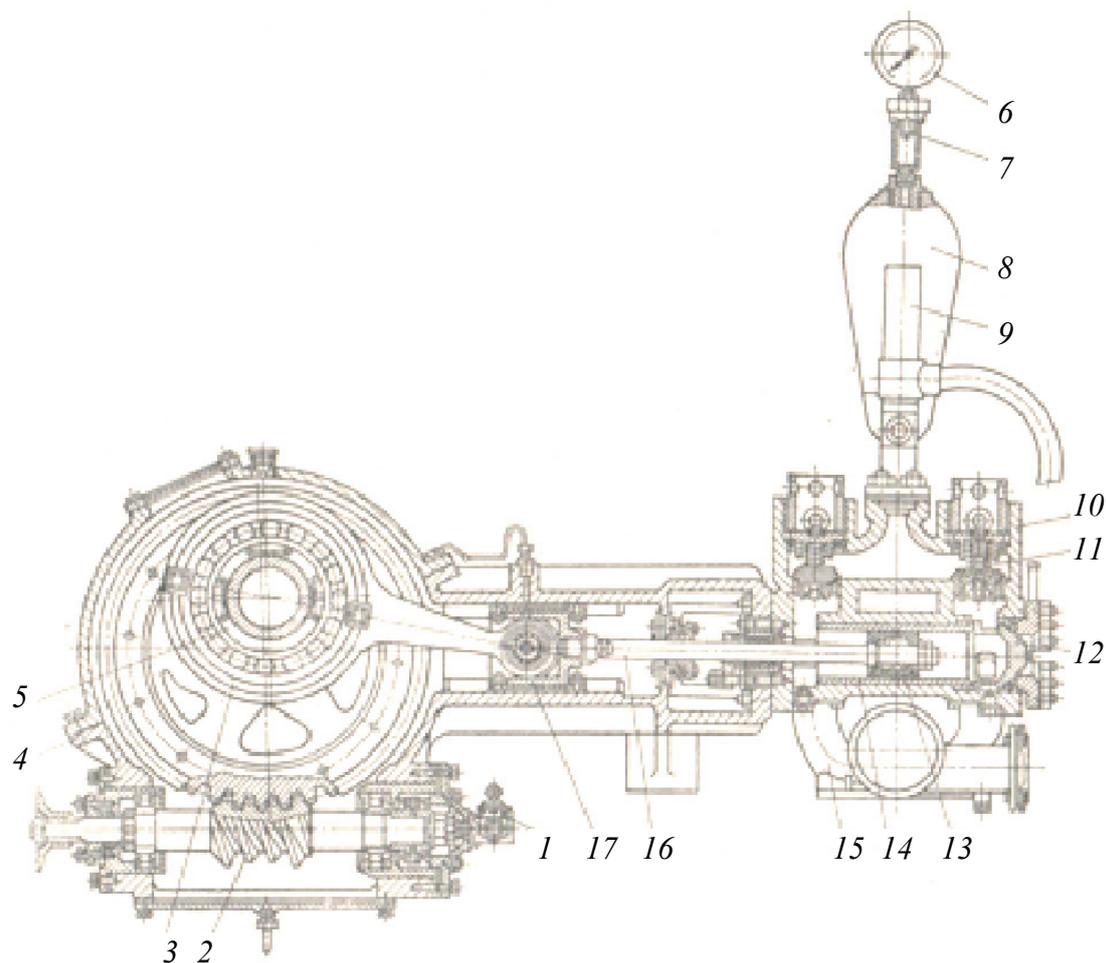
Цементирующий насос 9Т: 1 – коловратный насос; 2 – глобоидный червяк; 3 – шатун; 4 – станина; 5 – разъемный вкладыш; 6 – манометр; 7 – разделитель; 8 – коллектор нагнетательный; 9 – предохранительный клапан; 10 – клапанная коробка; 11 – клапан; 12 – коронка нажимная; 13 – поршень; 14 – втулка цилиндра; 15 – коллектор всасывающий; 16 – шток; 17 – крейцкопф
